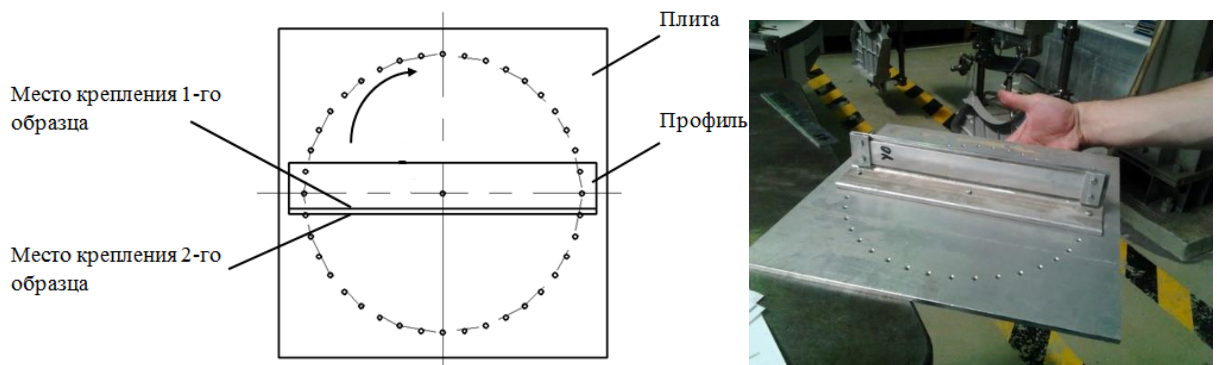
Схема закрепления образцов на имитаторе «Ребро»
